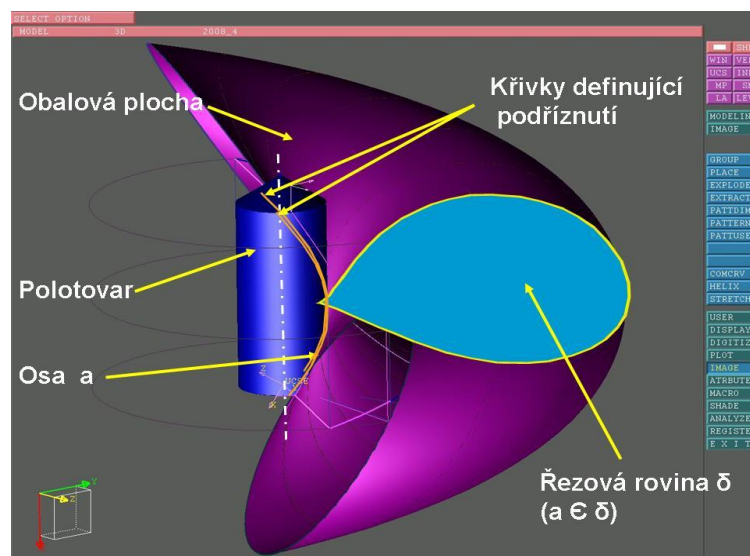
Příklad nástroje se šroubovitou drážkou
